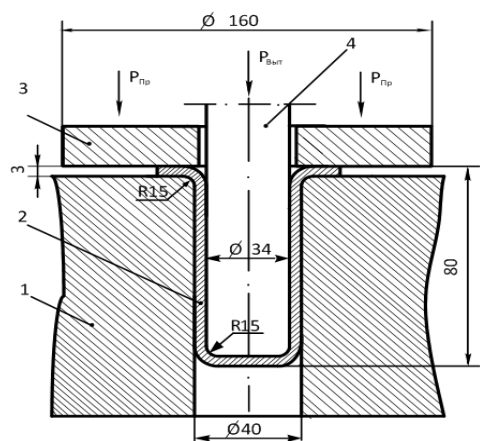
Геометрические параметры модели штампового инструмента для глубокой вытяжки листовых сталей с прижимом: 1 – матрица; 2 – заготовка; 3 – прижим; 4 – пуансон
